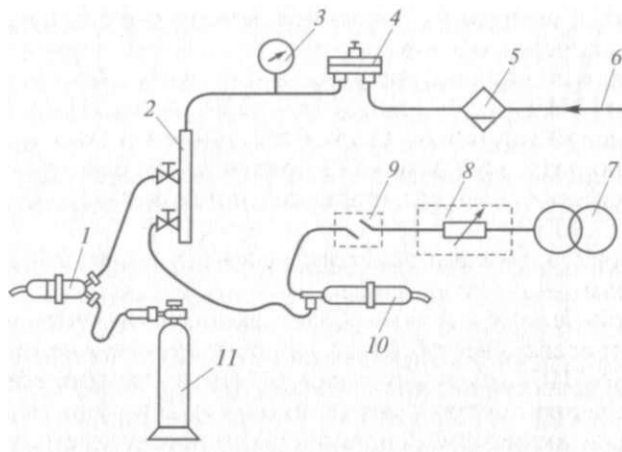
Схема питания горелок для прутковой сварки:
